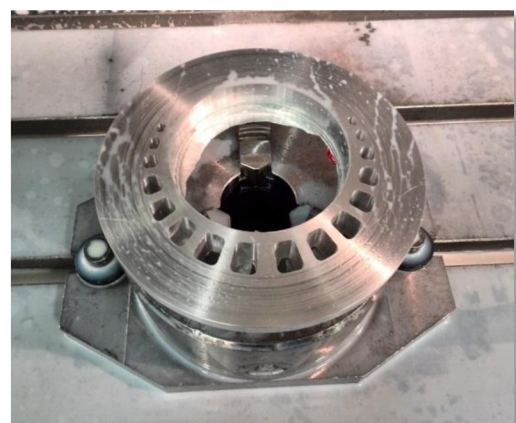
Tvar součásti po obrobení frézou o Ø 18 mm.
